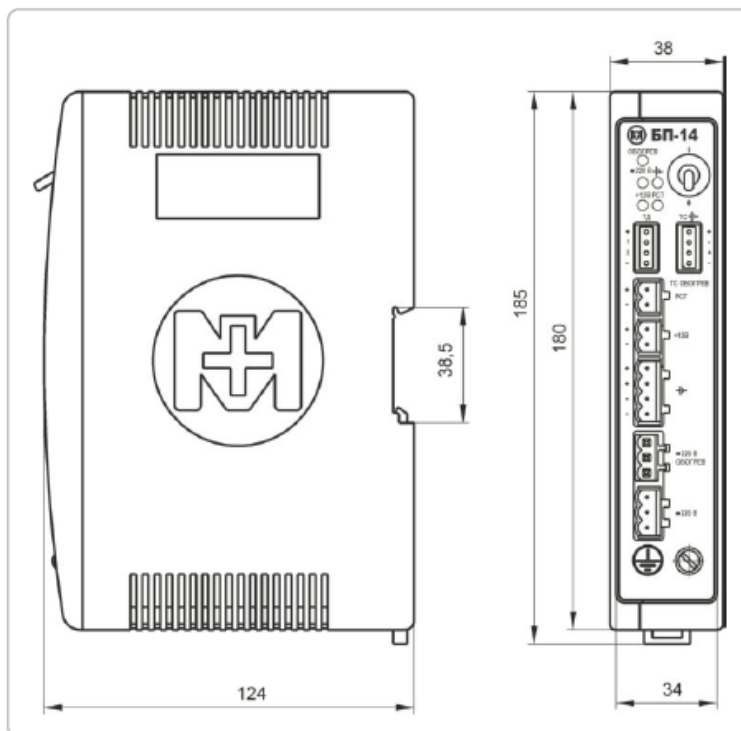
Внешний вид и габаритные размеры модуля БП-14
